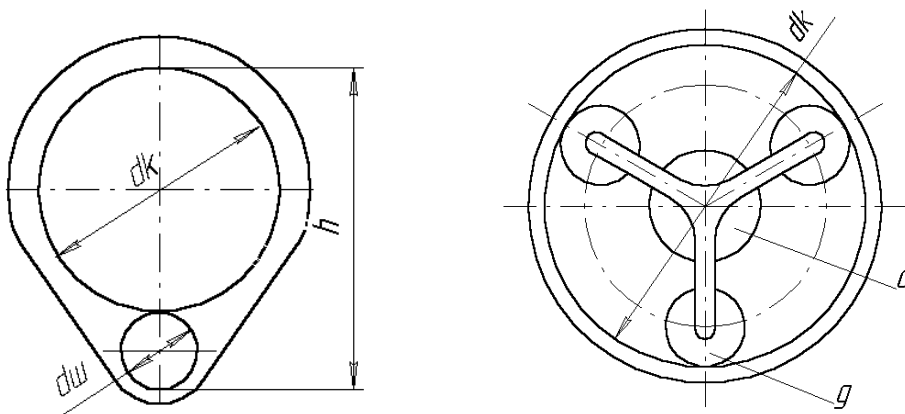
Схеми рядового та планетарного з передачею типу I редукторів
